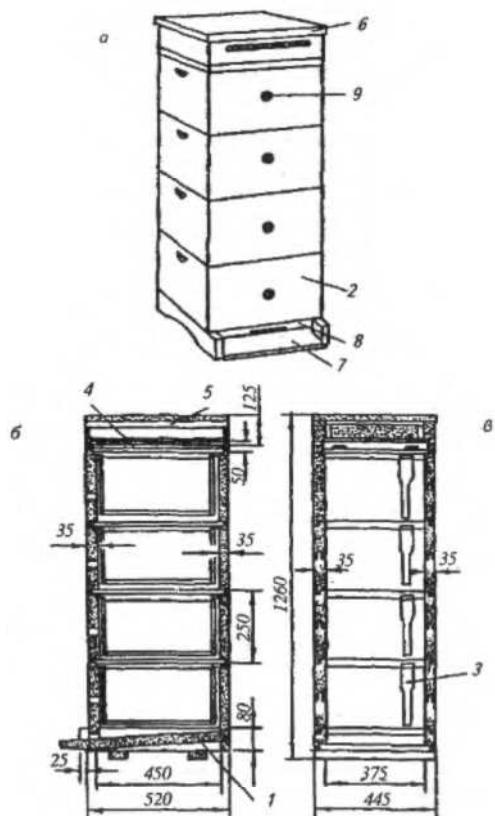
1. Многокорпусный улей: а — общий вид; б — продольный разрез; в — поперечный разрез (размеры в мм): 1 — дно; 2 — корпус; 3 — рамка; 4 — потолок; 5 — подкрышник; 6 — крыша; 7 — пролетная доска; 8 — петковый вкладыш; 9 — верхний петок; внизу — общий вид
